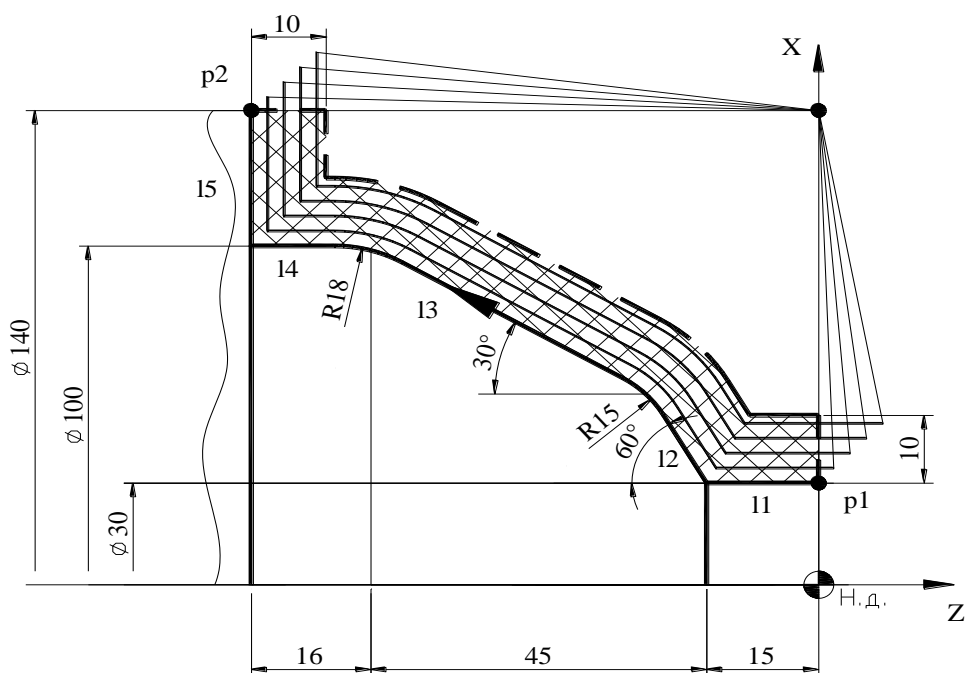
Схема удаления припуска при черновой обработке параллельной профилю
